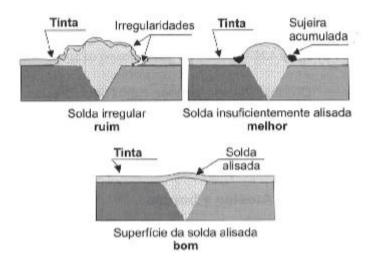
A superfície da solda deve ser analisada para diminuir a possibilidade de corrosão. Fonte: Manual CBCA – Tratamento de superfície e pintura.
